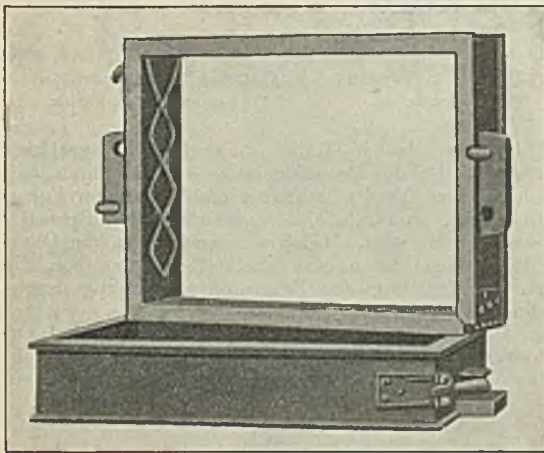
Abzugformkasten für Berkshirermaschinen.
